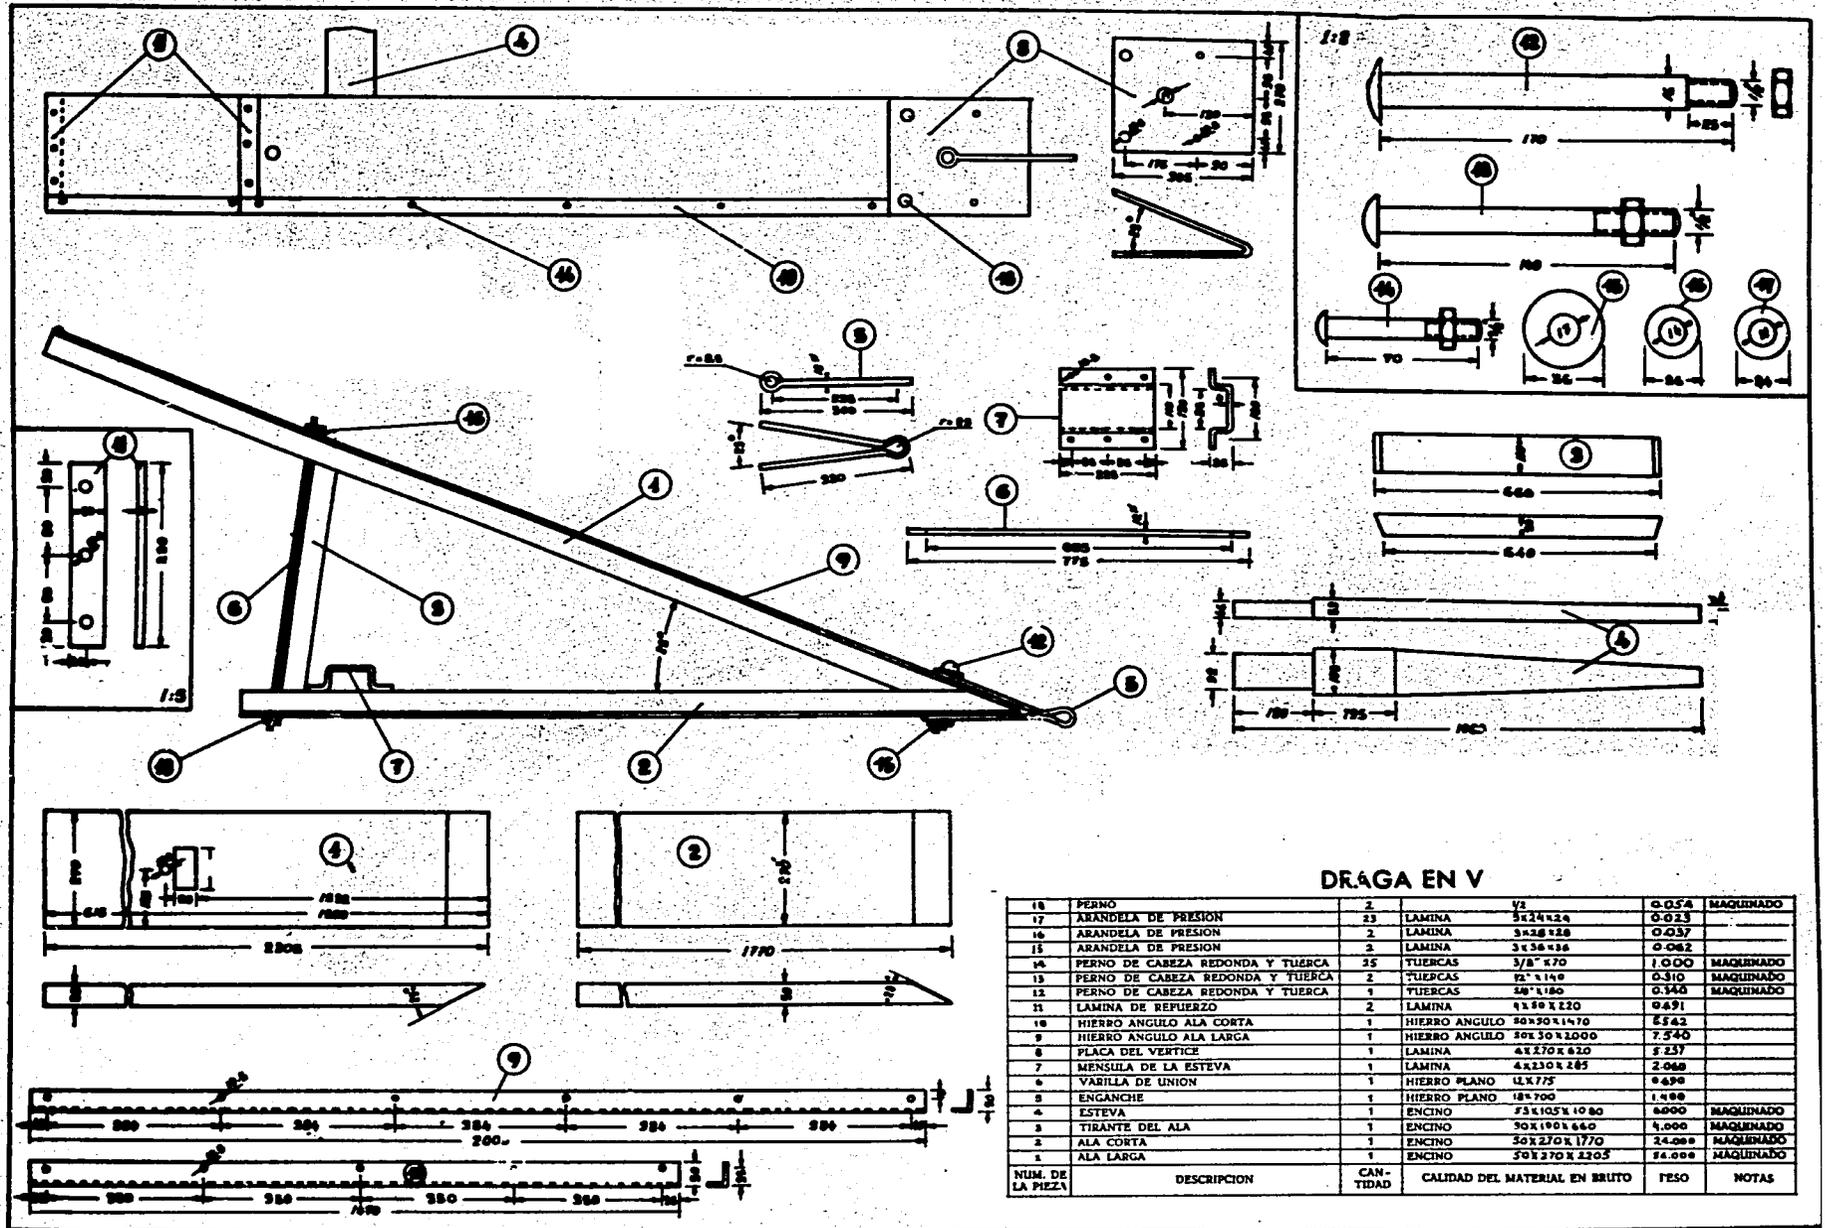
DETALLES DE CONSTRUCCION PARA LA DRAGA EN V
